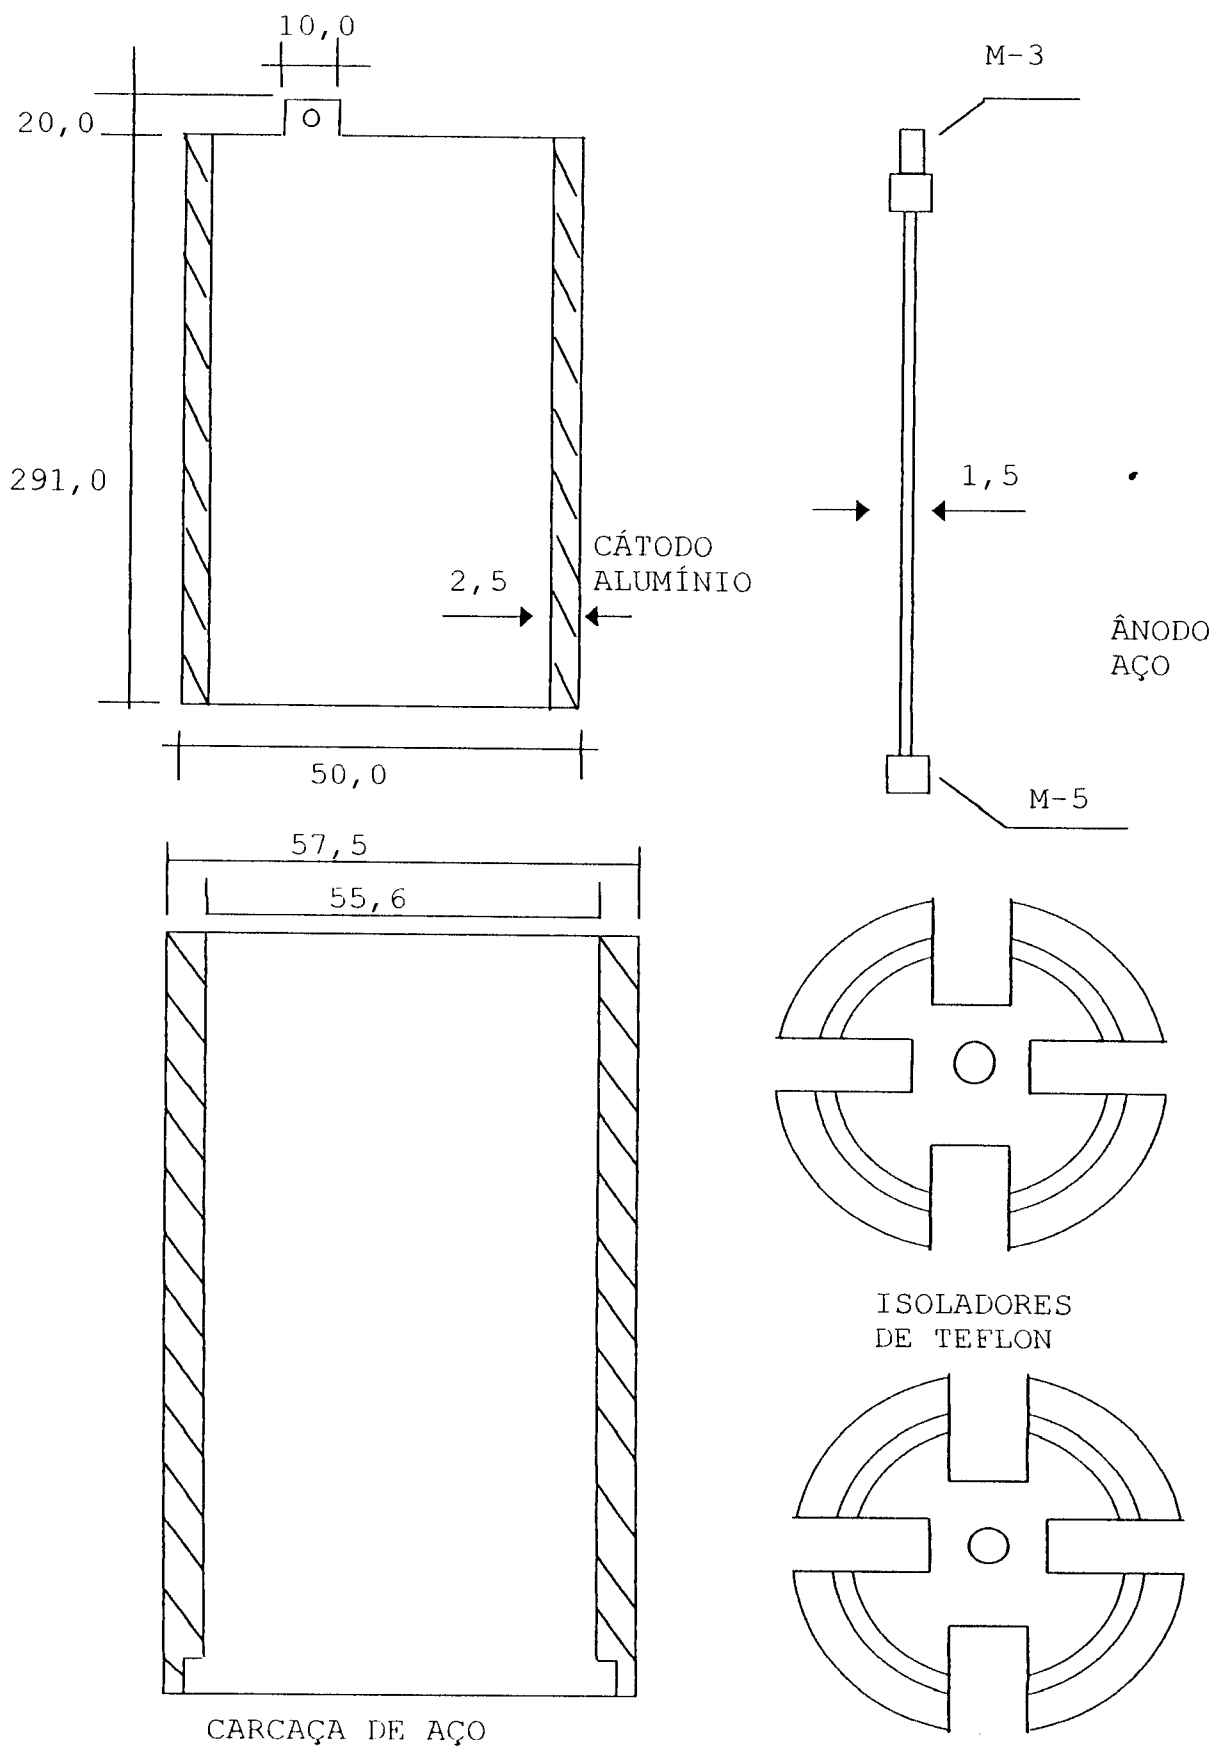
Esboço das Partes que Compõem a CIGEVaP.
